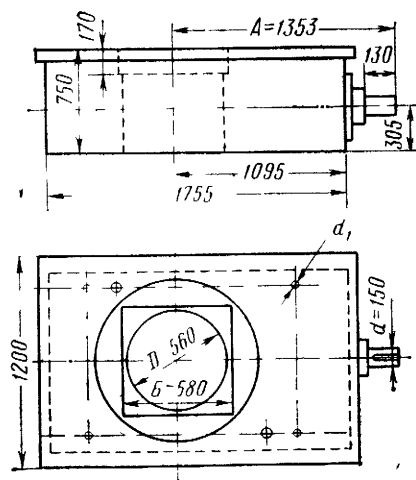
Присоединительные размеры ротора Р560-Ш8
